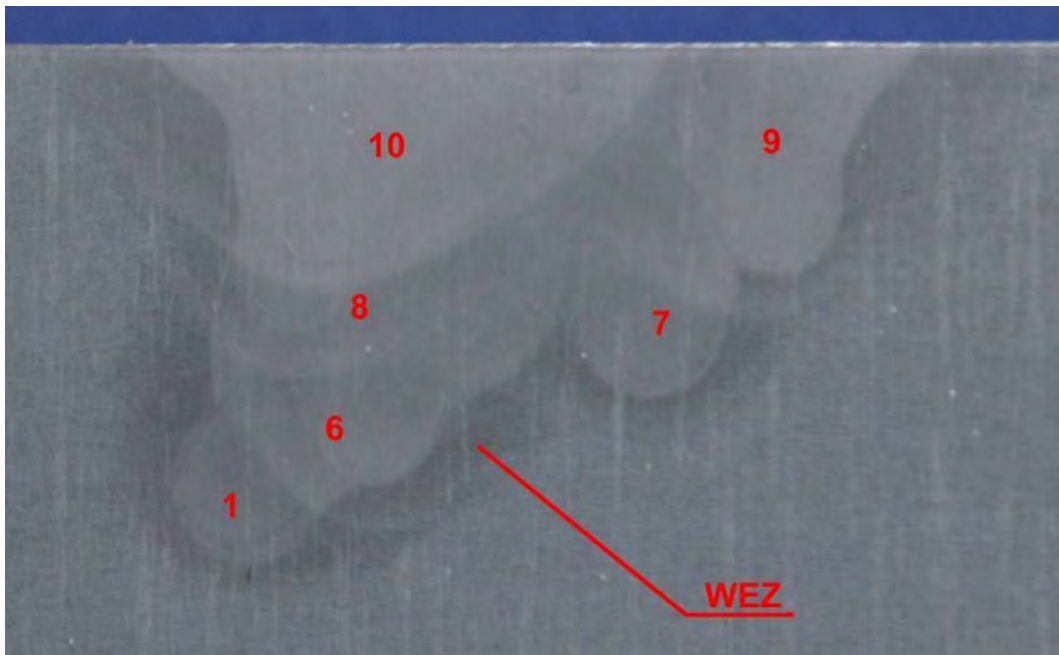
Probe 01 - Ansicht oberer Teil der Schweißnaht
